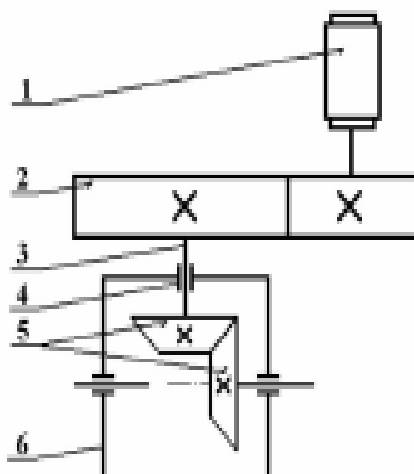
Кинематическая схема привода с коническим зубчатым редуктором
